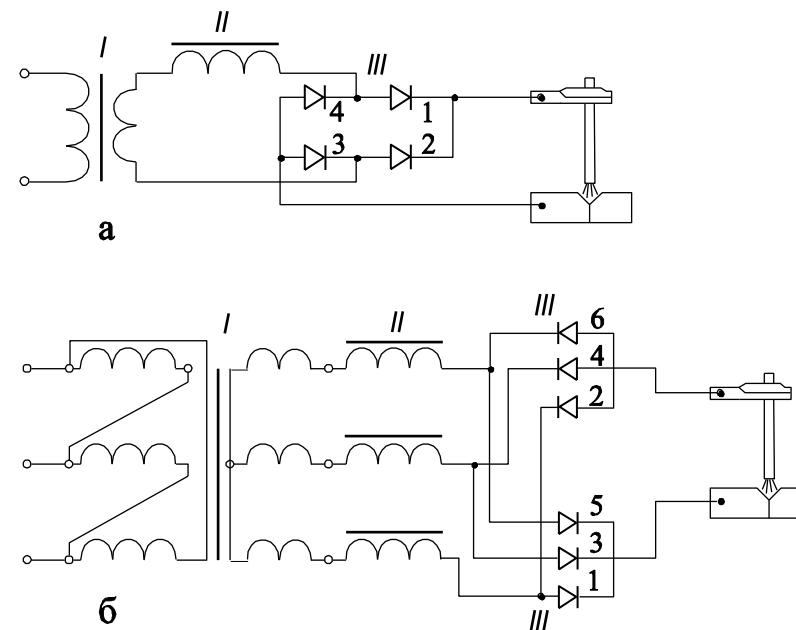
Принципиальные схемы сварочных выпрямителей: а - однофазного, б - трехфазного. I - понижающий трансформатор; II - устройство для регулирования напряжения; III - блок вентилей.
